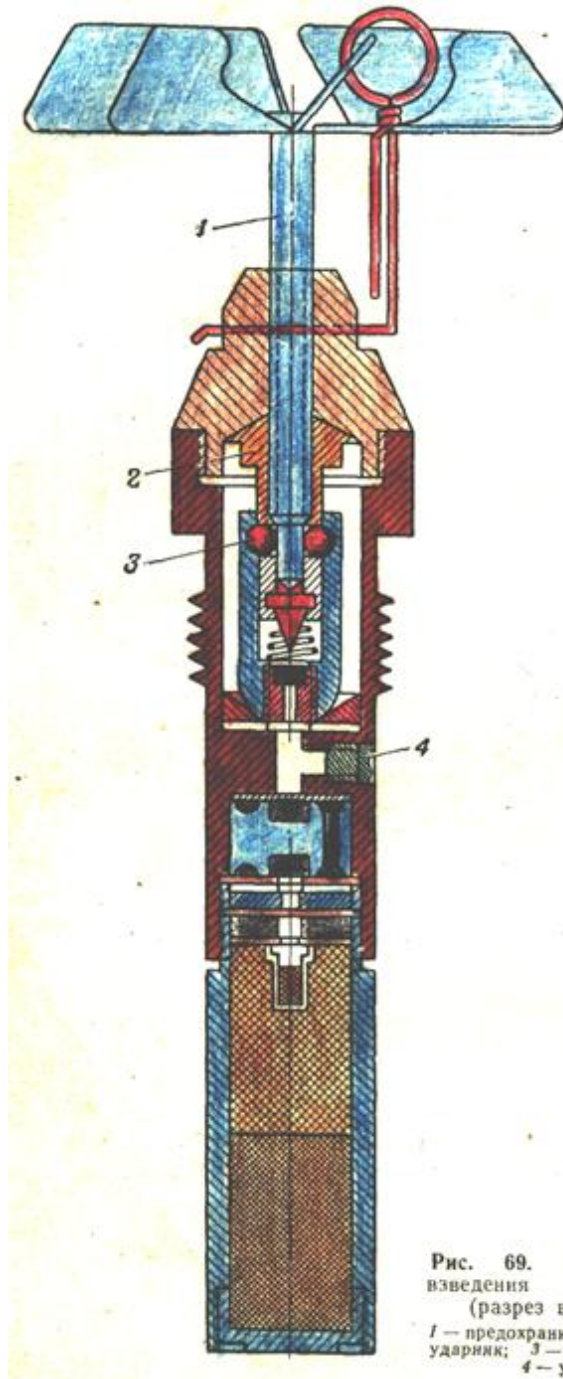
Ветряночный механизм взведения головного взрывателя (разрез взрывателя АВ-1д/у):
